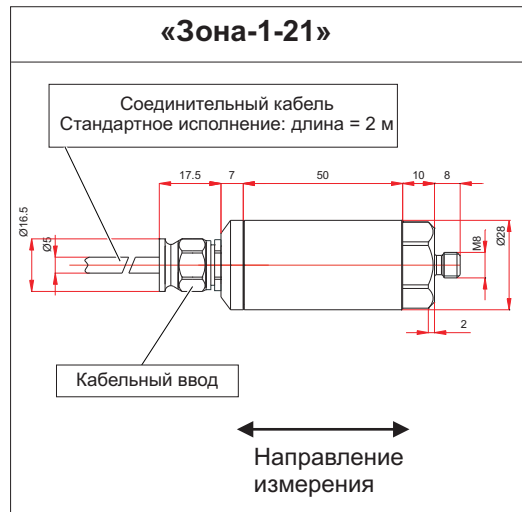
Размеры корпуса и направление измерения: «Зона-1-21»
